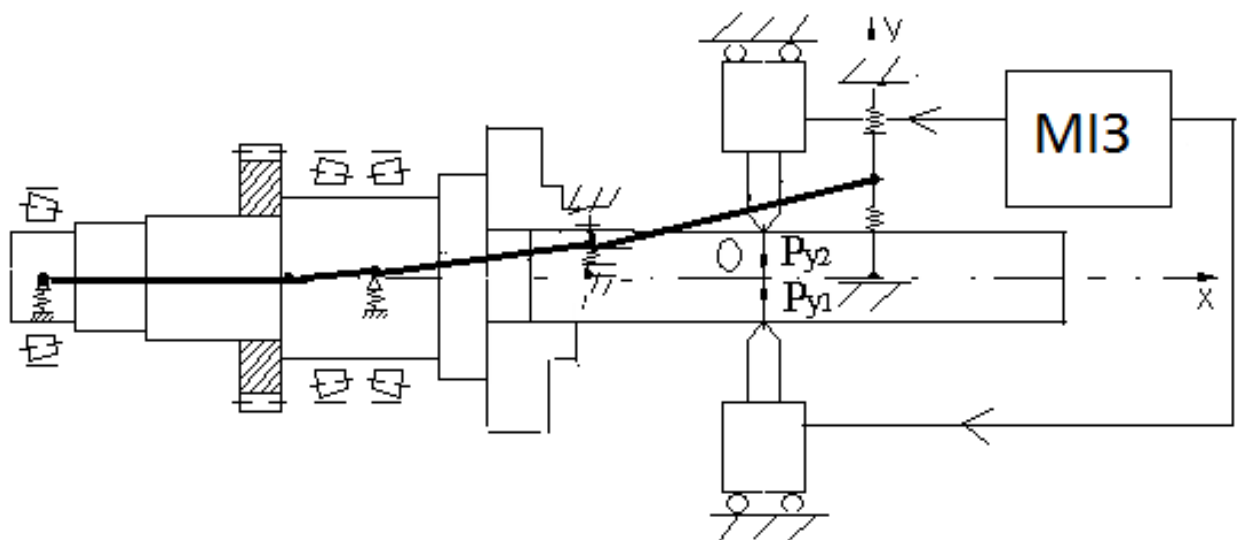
Розрахункова схема дворізцевого самоналагоджувального пристрою в рамках динамічної підсистеми оброблюваної заготовки
